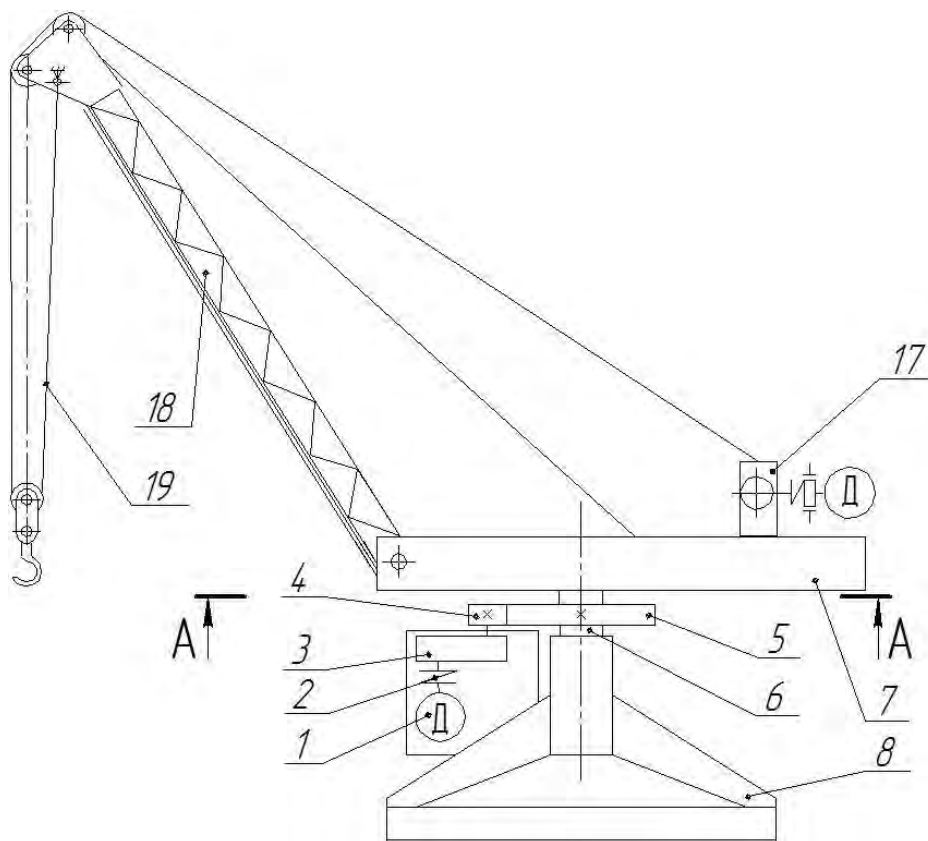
Стріловий кран: 1 – двигун; 2 – пружна муфта; 3 – редуктор; 4 – шестерня; 5 – опорно-поворотний круг; 6 – поворотний вал; 7 – поворотна частина; 8 - рама.
